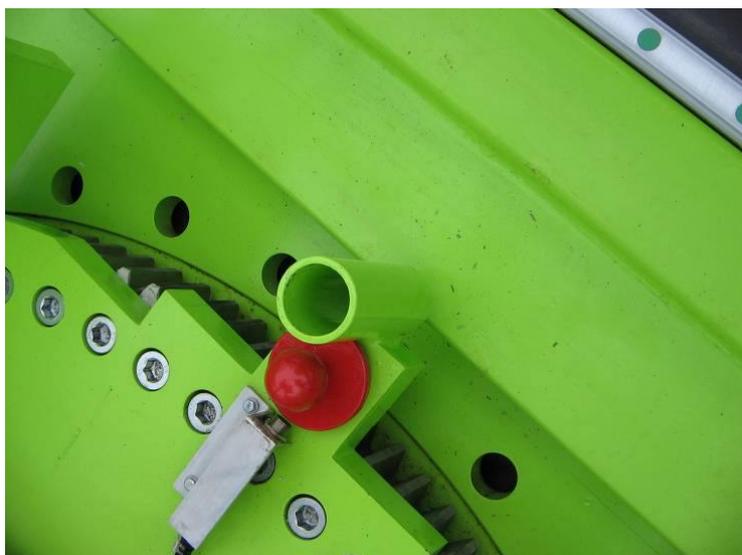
Steckbolzen zu Drehkranz Kabelabrollbock
